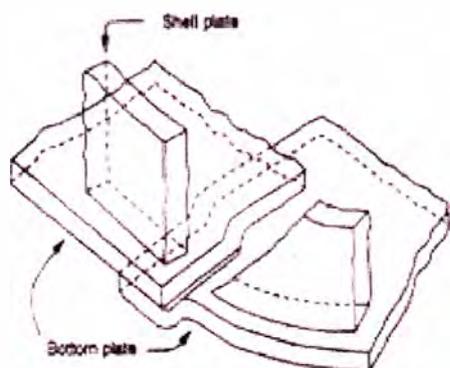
a Esquema soldadura API-650 para solapado de chapas bajo envoltente
